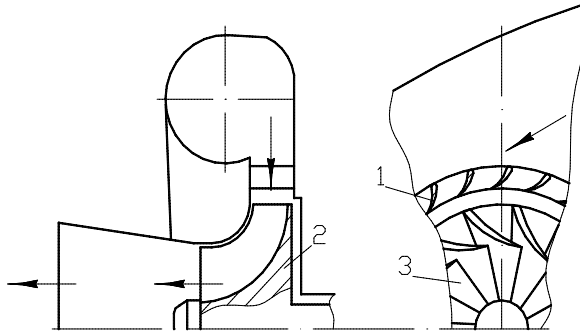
Схема центроостремительной турбины: 1 – решётка неподвижных лопаток; 2 – диск; 3 – решётка рабочих лопаток.
